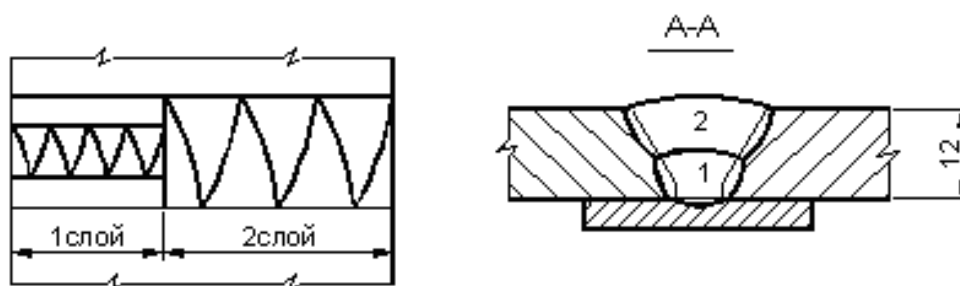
Схема сварки в 2 слоя.
